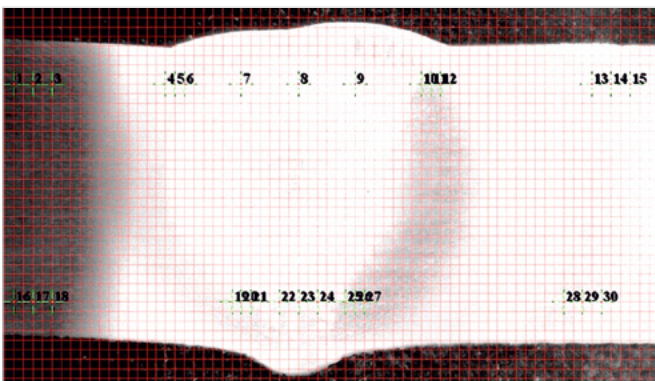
Схема замера твердости сварного соединения. Цифрами указаны номера точек замера твердости
